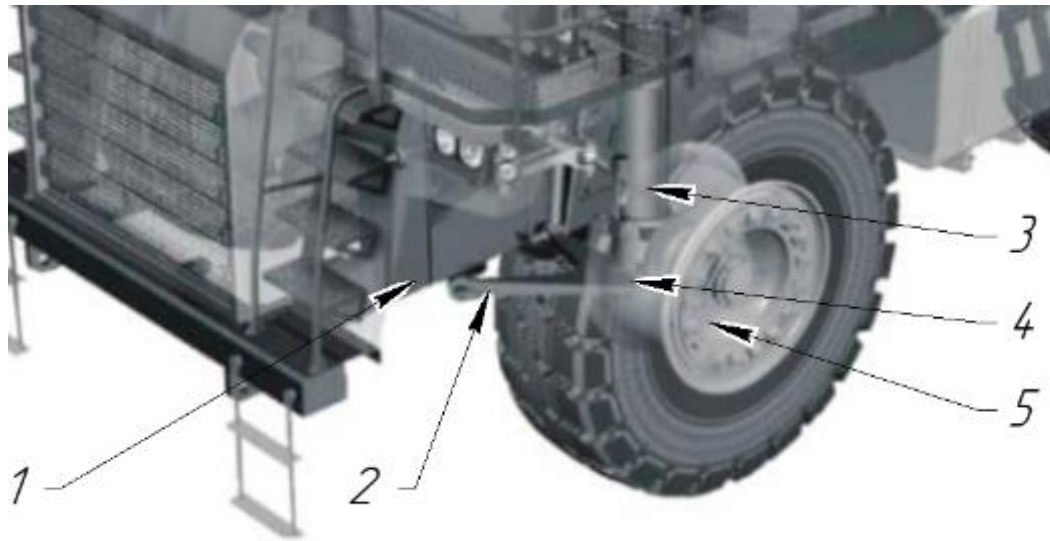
Внешний вид подвески SANY SET230. 1 – рама; 2 – поперечный рычаг; 3 – пневмогидравлический упругий элемент передней подвески; 4 – поворотный шкворень; 5 – ступица
